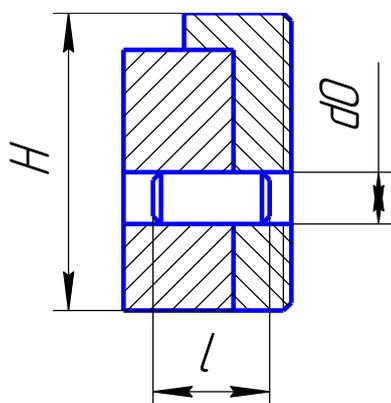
Соединение гайки с корпусом с помощью штифта
